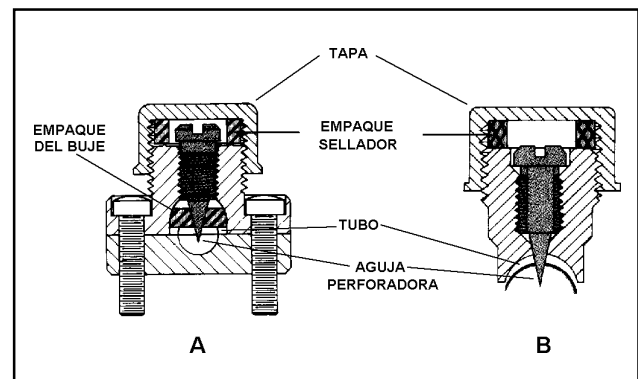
Válvulas perforadoras típicas. (A) atornillada, (B) soldable.
